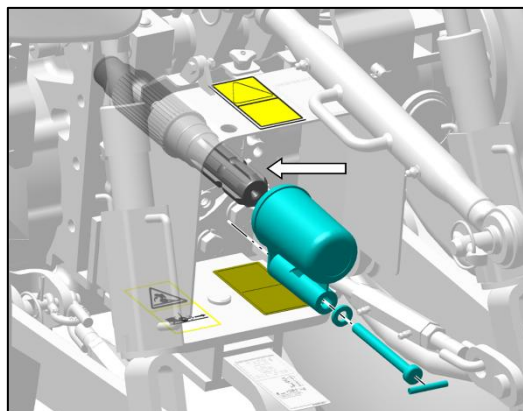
HINTERE ZAPFWELLE MIT ZAPFWELLENKAPPE
